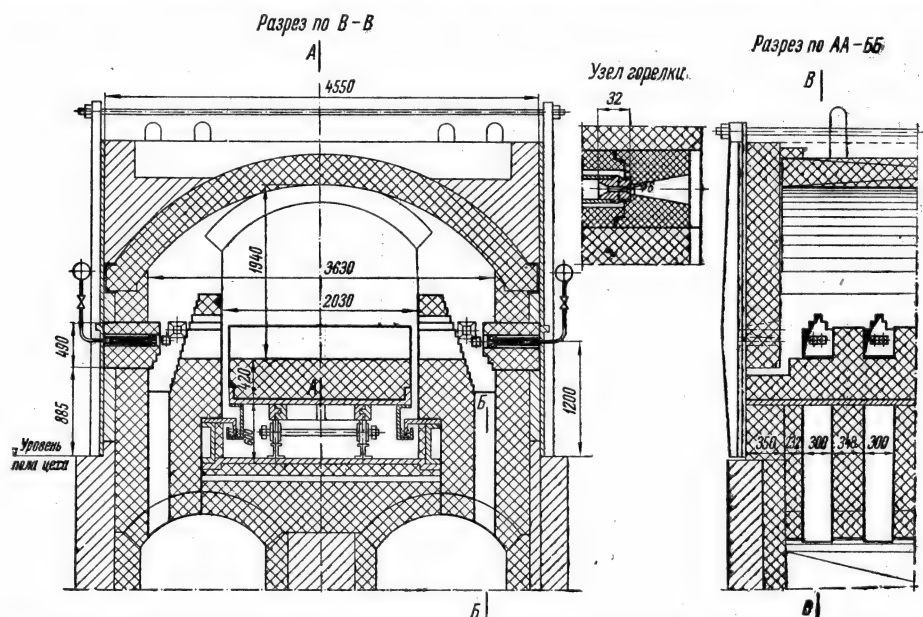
Переоборудование на газовое топливо камерной регенеративной печи с выдвижным подом.
